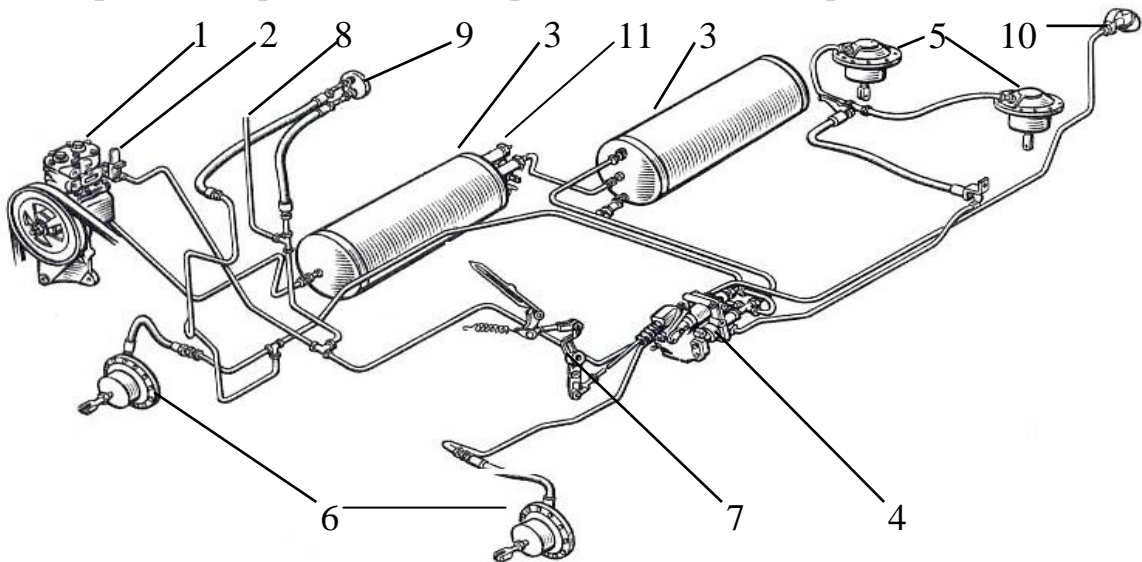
Одноконтурный пневматический привод рабочей тормозной системы грузового автомобиля: 1 – компрессор; 2 – регулятор давления; 3 – ресиверы; 4 – тормозной кран; 5 – тормозные камеры задних колес; 6 – тормозные камеры передних колес; 7 – педаль; 8 – трубопровод отбора воздуха на привод стеклоочистителей; 9 – манометр; 10 – соединительная головка для подключения тормозной системы прицепа; 11 – предохранительный клапан
